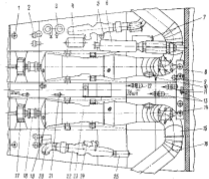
Конструкция авиационного двигателя газотурбохода «Буревестник»: 1 — осевой вал; 2 — компрессор; 3 — входной бак; 4 — раздаточный бак; 5 — турбокомпрессор; 6 — бакстартер и турбина; 7 — масляный насос; 8 — компрессорный радиатор; 9 — бак; 10 — пневмомоторы; 11 — насос ШИП-11; 12 — масляный насос ШИП-104; 13 — масляный насос ШИП-11; 14 — агрегат ШИП-11; 15 — масляный холодильник; 16 — масляный трубопровод главного двигателя; 17 — пневмомотор ЭСА-105; 18 — упорный подшипник; 19 — охлаждающая муфта вспомогателя; 20 — главный двигатель АИ-20А; 21 — пружина ГС-100; 22 — входной насос ШИП-104; 23 — трубопровод ТГ-16; 24 — бакстартер авиационного топлива; 25 — масляный холодильник ТГ-16; 26 — пневмомоторы ПНО-100.
